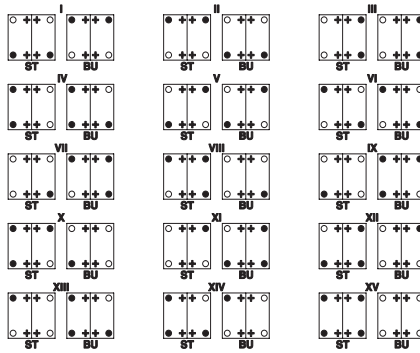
Механический ключ из втулки и штифта для корпусов с двумя контактными вставками
